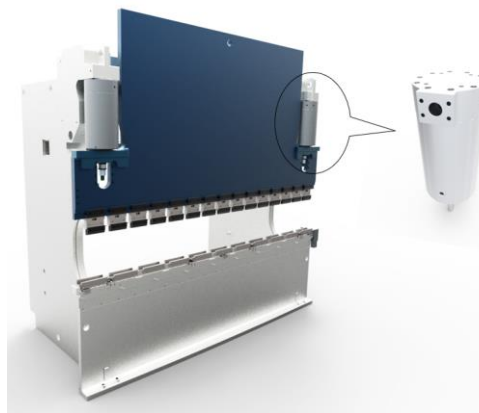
Quinadora Adira que utiliza cilindro hidráulico de corpo redondo.
